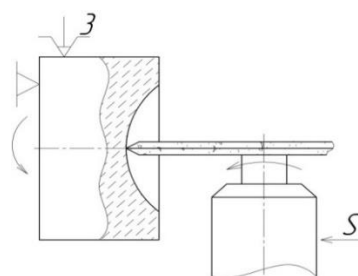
Схема обработки внутренней сферической поверхности алмазно-отрезным кругом
